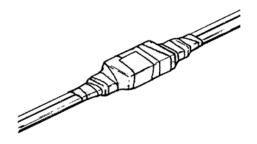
Обмотка соединителя UDW2 лентой 88T.
